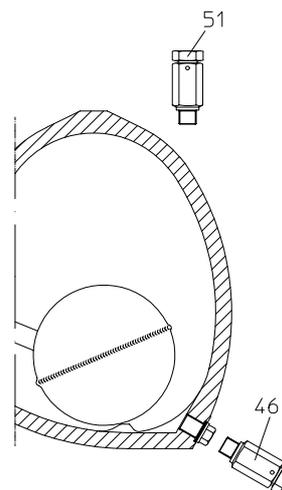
1 mit Flanschen - horizontale Einbaulage
